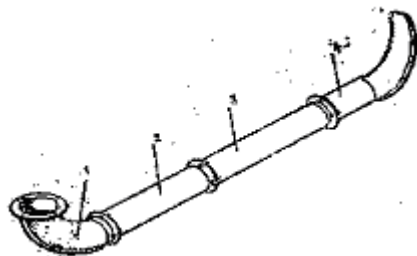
Пневмотранспортер: 1 - колено; 2, 3 — трубы; 4 — носок
